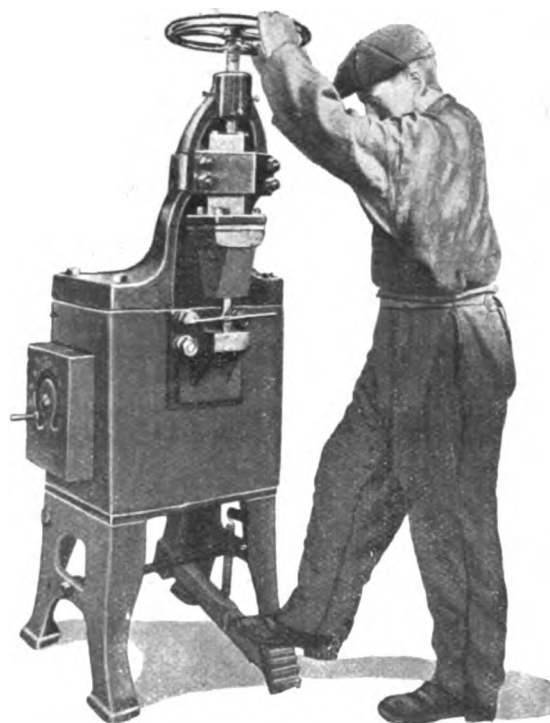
Vue d'une machine à souder par points avec commande à pédale (La Soudure électrique).
